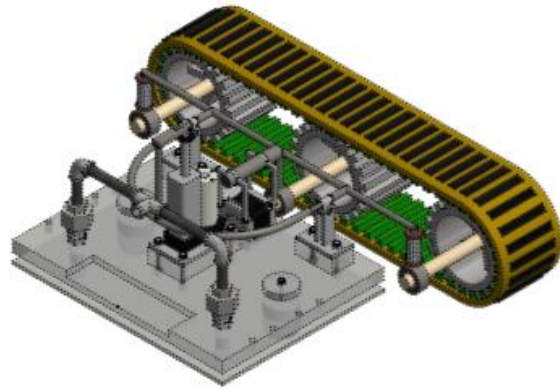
Detalle de rodaje horizontal, vista isométrica
